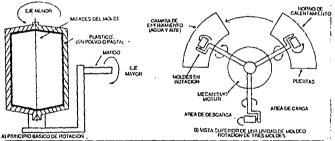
Moldeo rotacional, (Ref. 26).
